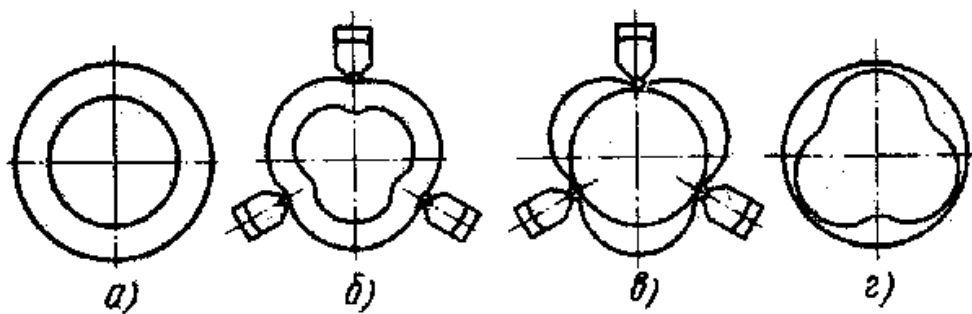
а) - заготовка до установки на верстаті; б) - після закріплення в трикулачковому патроні; в) - після обробки; г) – після
